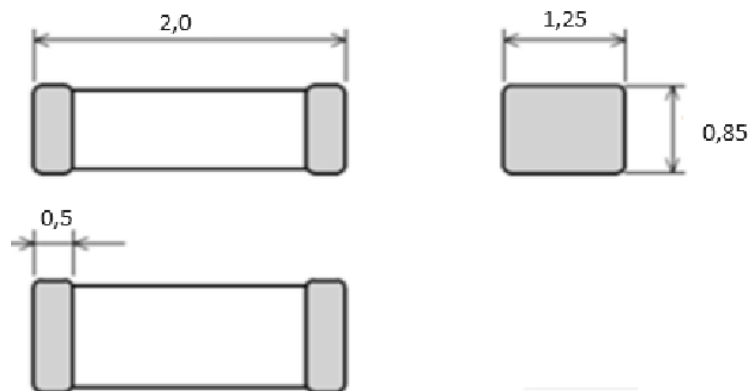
Зовнішній вигляд та габаритні розміри дроселя BLM21AG102SN1 в корпусі SMD0805
